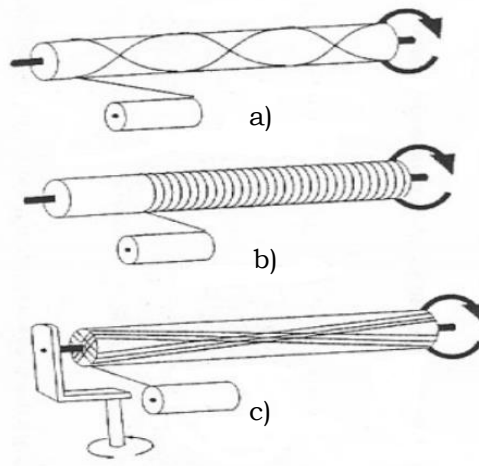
a) Bobinado helicoidal, b) Bobinado circular, c) Bobinado polar.
